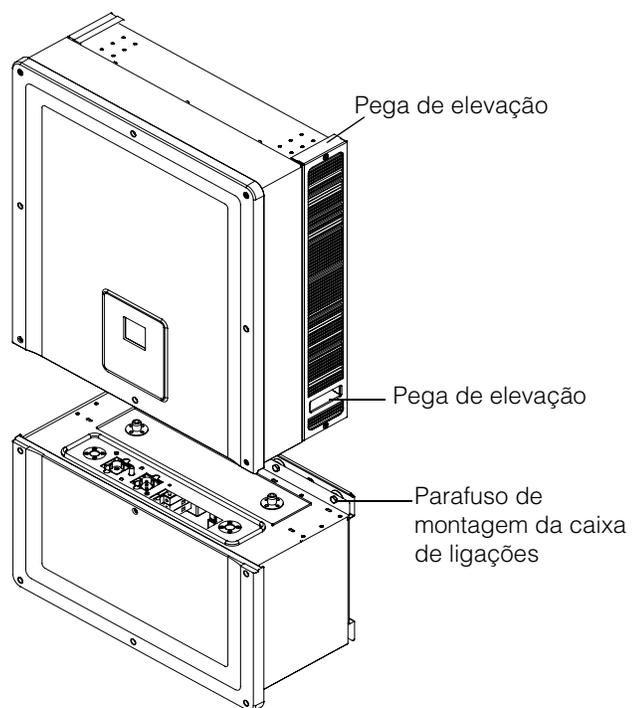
Inversor e caixa de ligações – Vista explodida
